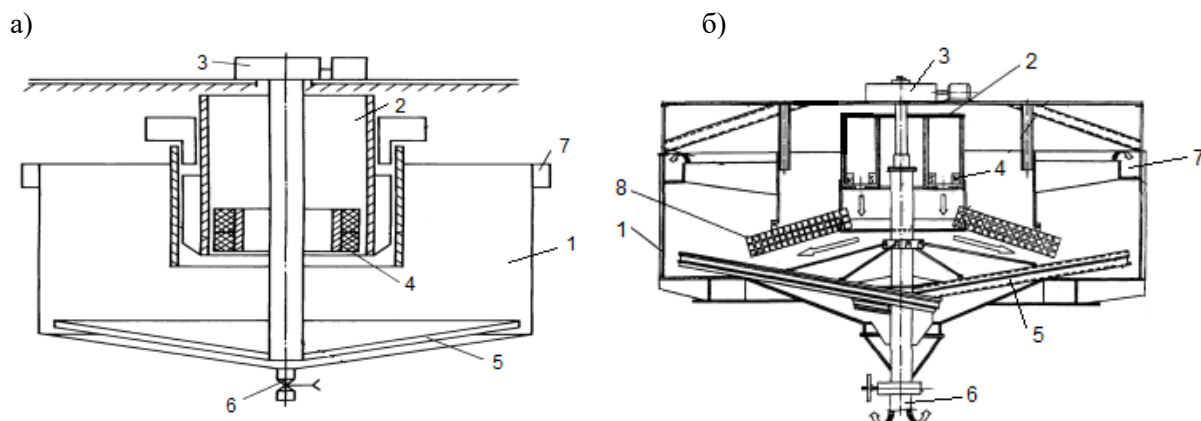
Конструктивные схемы магнитных аппаратов: а) магнитный дешлампатор МД-9; б) – магнитный гидросепаратор МГС-9: 1 – чан; 2 – загрузочный бак; 3 – привод граблин; 4 – магнитная система; 5 – граблины; 6 – разгрузочное устройство; 7 – желоб сливной; 8 – дополнительная магнитная система
